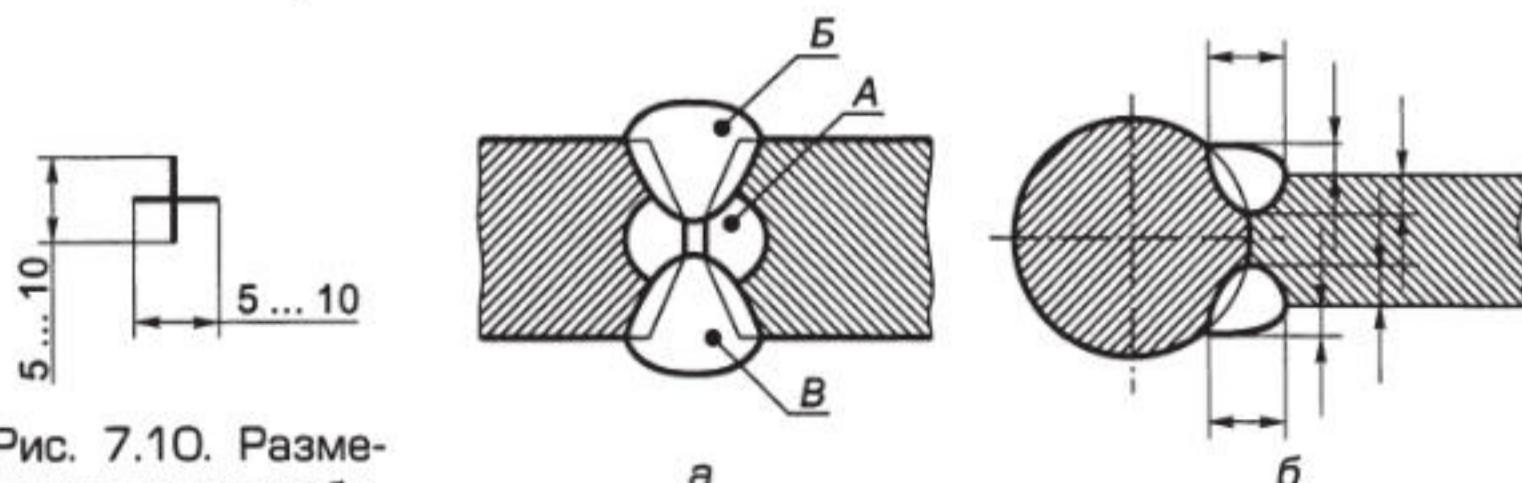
Размеры условного обозначения одиночной сварной точки
